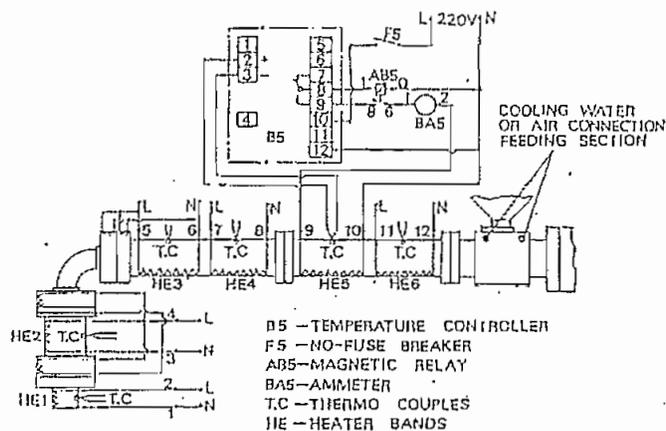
Sistema de calentamiento de máquina extrusora (ref. 12)
